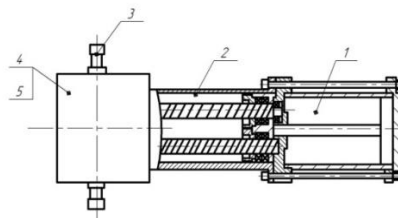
Шестипозиционная резьбонарезная головка станка
